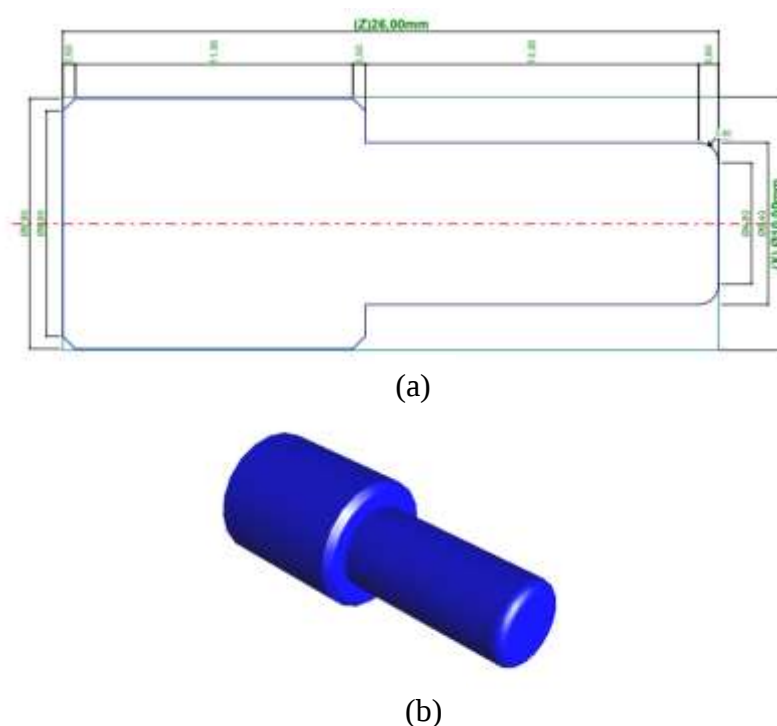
(a) Desenho do eletrodo de 6,4 mm em corte (2D) e (b) perspectiva 3D do eletrodo pronto para usinagem CNC.
